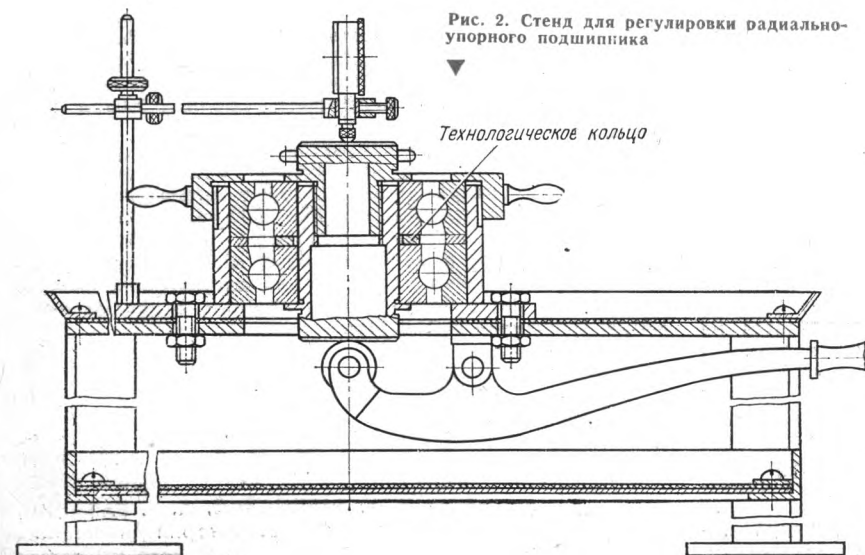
Стенд для регулировки радиально-упорного подшипника
